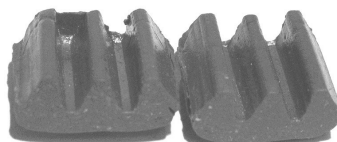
Фотография общего вида слепков зубьев шестерни и колеса
